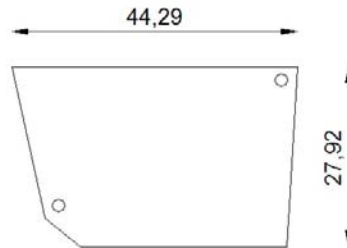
Dimensiones de del circuito impreso PCB2.
